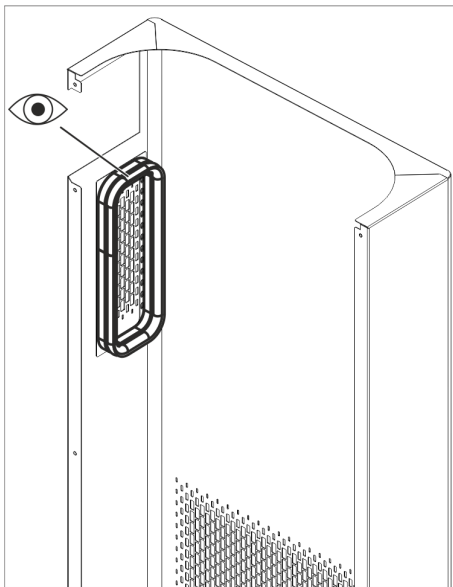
Comprobación de la empaquetadura en la tubuladura de aire
